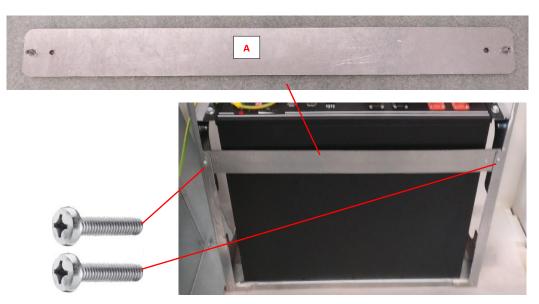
Installazione staffa segregazione batterie sul WALL-BOX-Bx BASE
